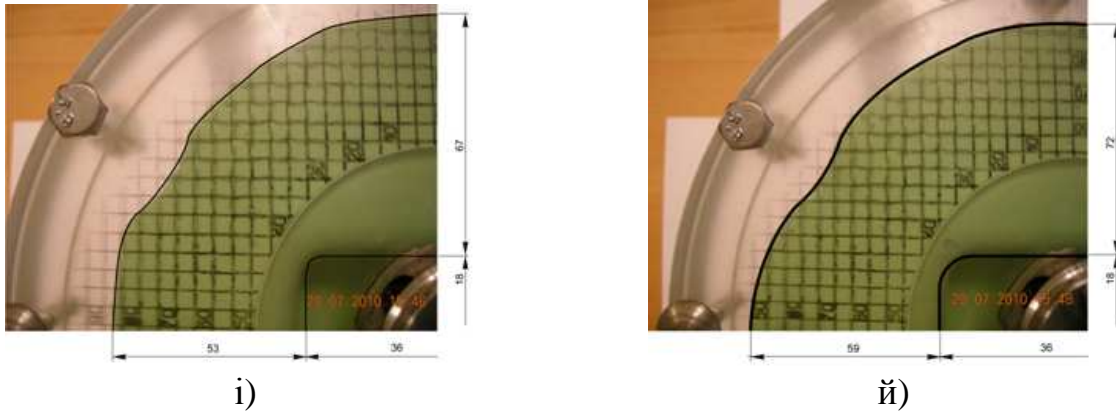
Результати “зворотного” витягування при різній глибині умовної коробчатої деталі прямокутної форми з розмірами у плані 72x36 мм.
